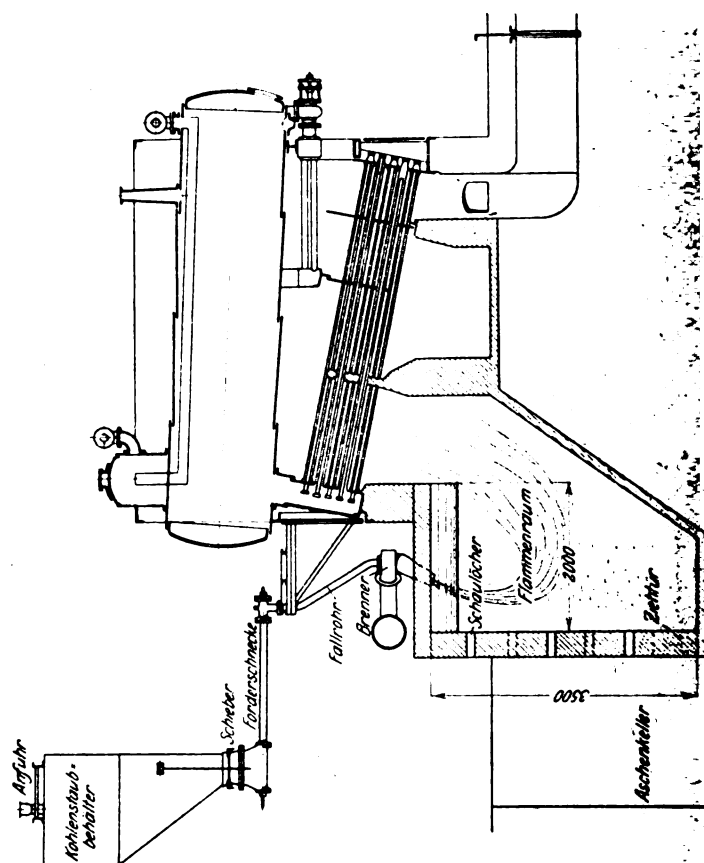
Kohlenstaubfeuerung der Am. Industrial Eng. Co., Chicago.
